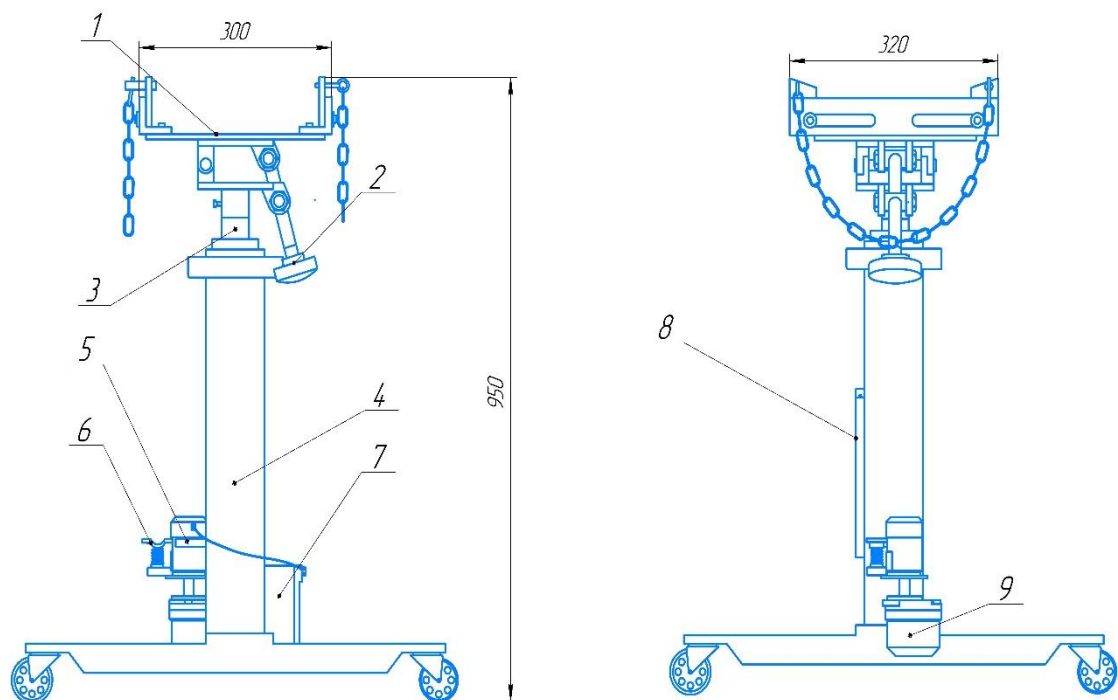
Схема конструкции на базе Berger BG 1276
